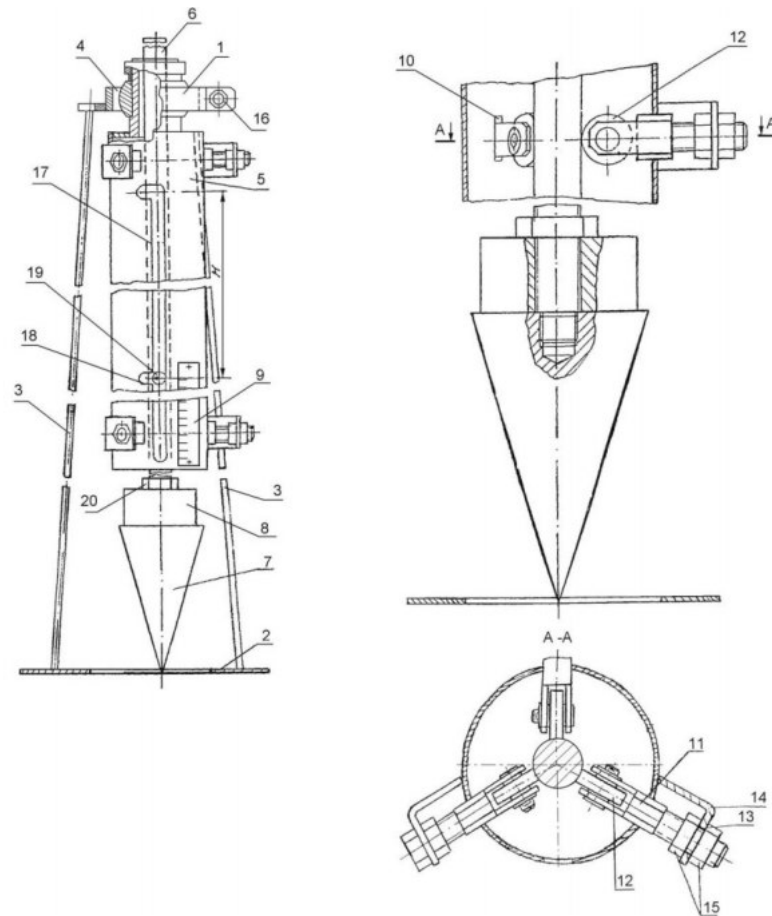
Твердомер предлагаемой конструкции:
